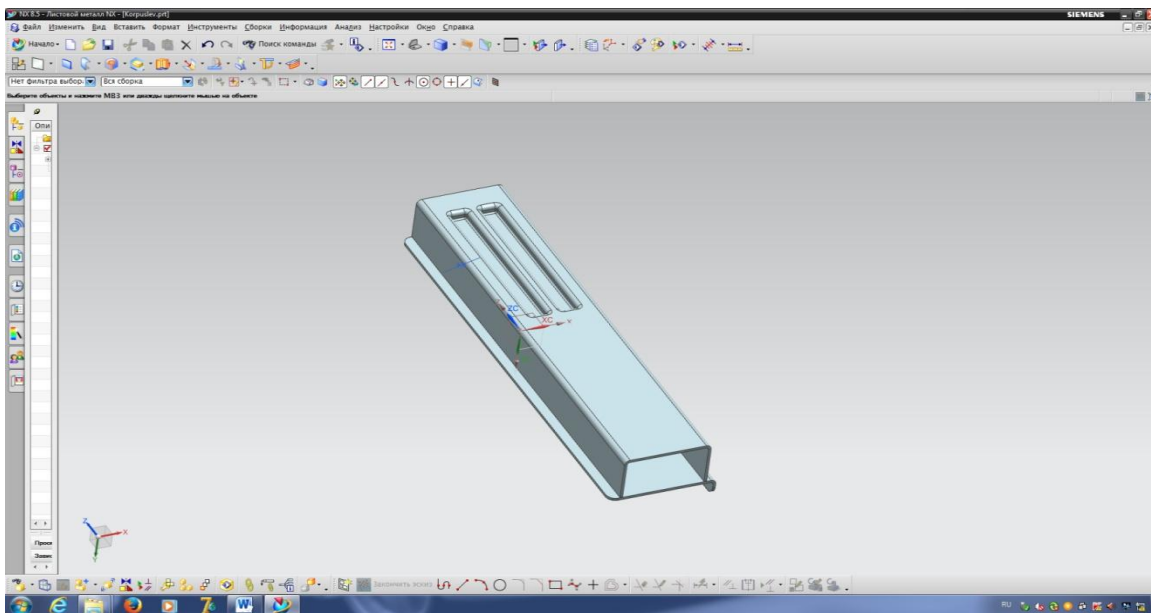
Сборка «корпус» и «лист передний и задний».
